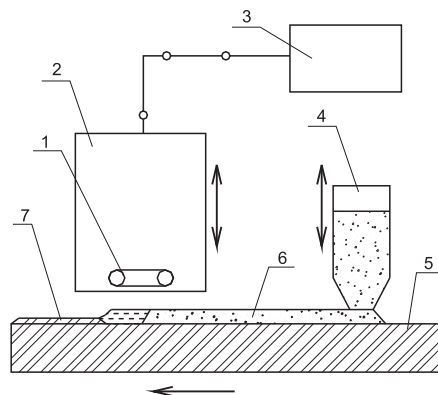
Упрощенная технологическая схема процесса наплавки, где 1 – индуктор, 2 – нагревательный контур, 3 – ВЧ генератор, 4 – дозатор, 5 – наплавляемая деталь, 6 – наплавляемый порошок, 7 – упрочненный слой
